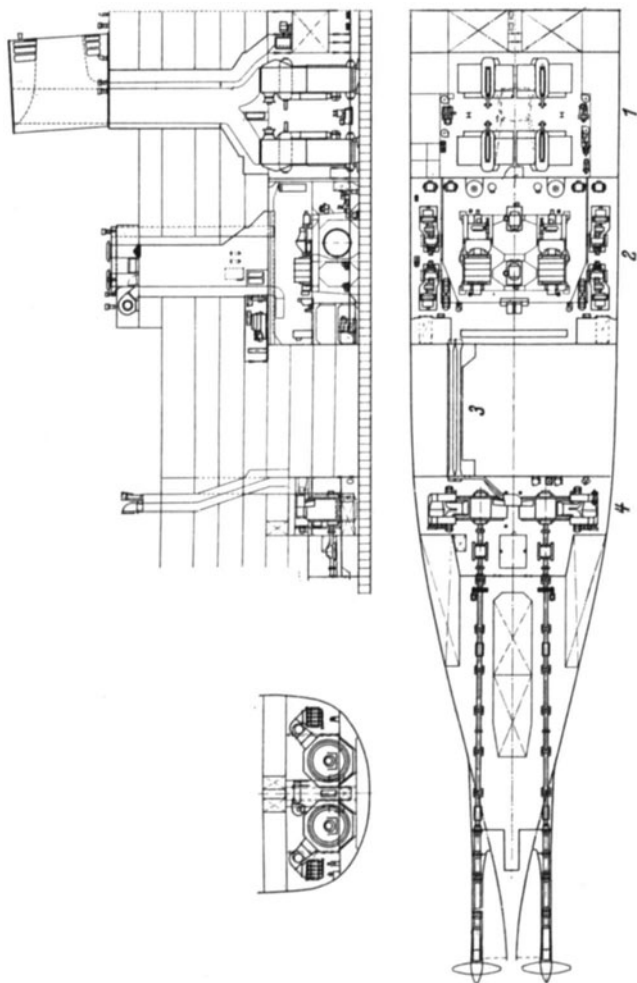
Plan der Hauptmaschinenanlage eines turboelektrisch angetriebenen Schnell dampfers (Deschimag, Bremen).
